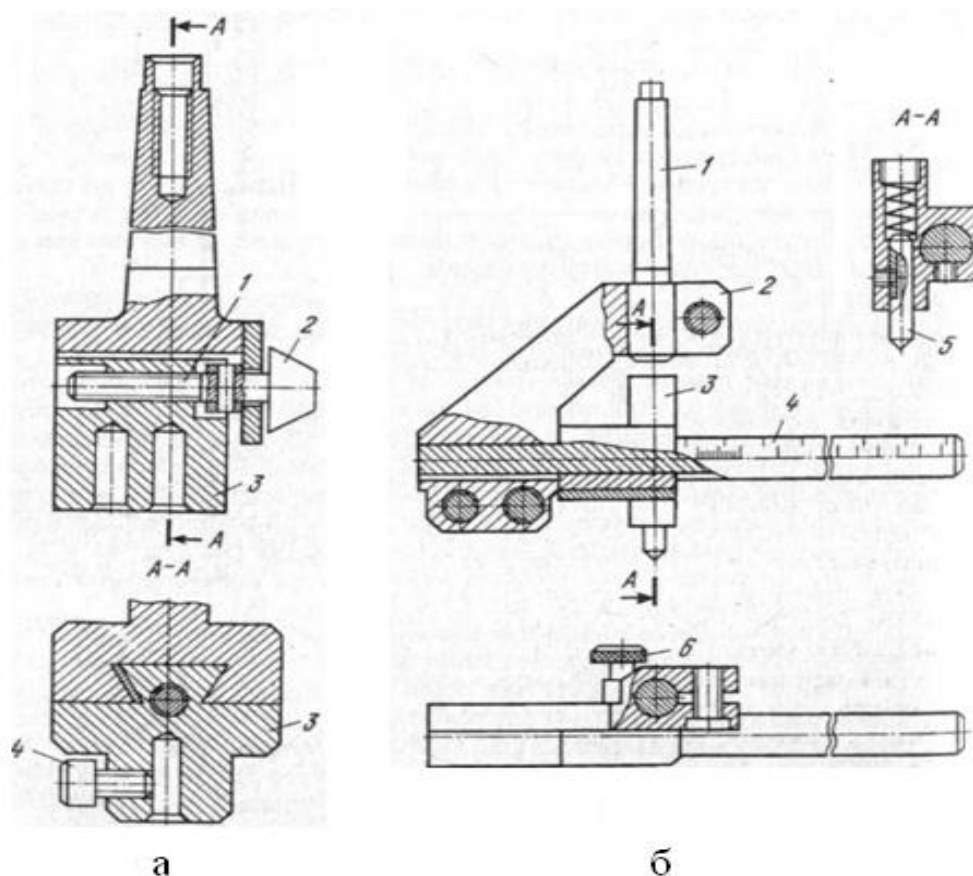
Приспособления координатно-расточных станков: а - расточные головки, б – рискообразователи.
